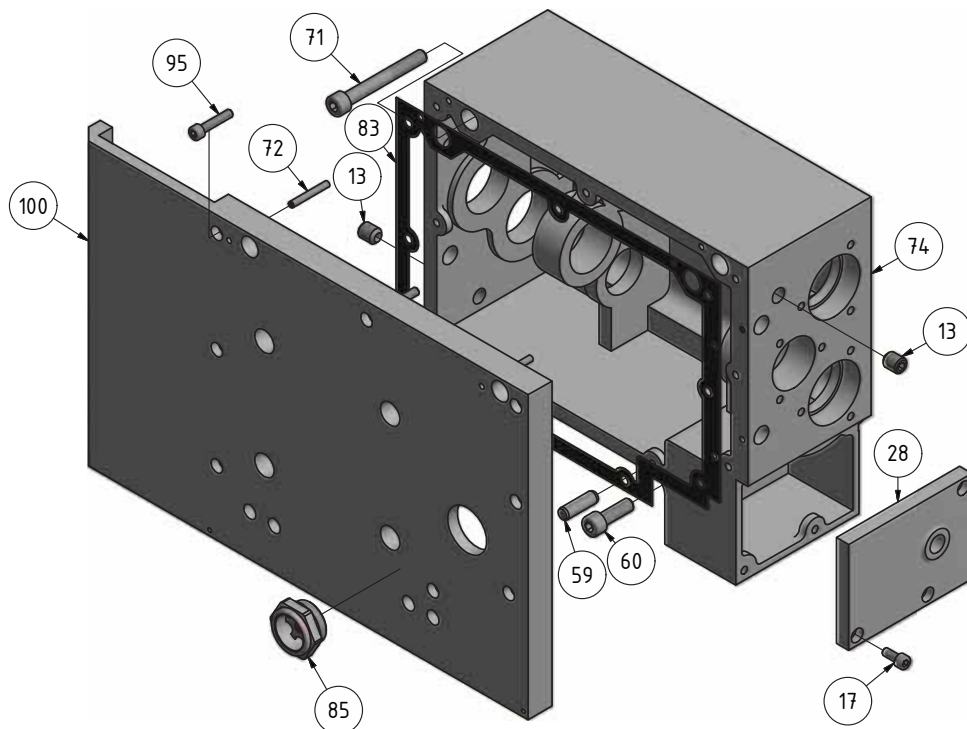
Vorschubgetriebe 1-6 - Feed gear 1-6
